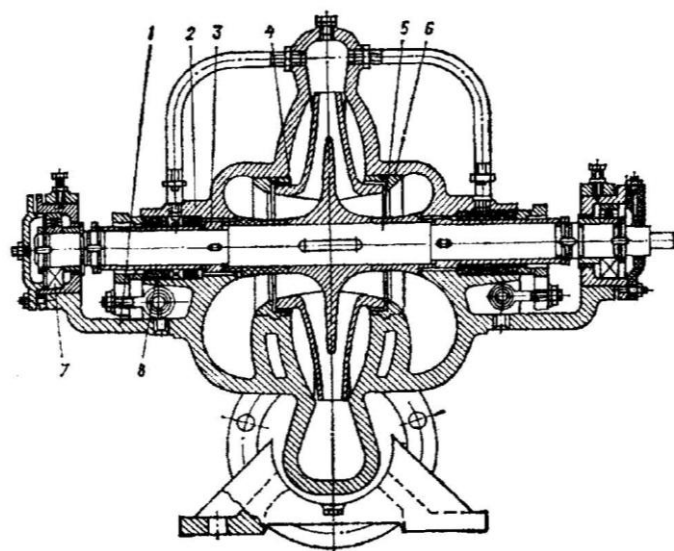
Горизонтальный центробежный насос типа Д: 1 – корпус, 2 – крышка, 3 – защитная втулка, 4 – рабочее колесо, 5 – вал, 6 – уплотнительное колесо, 7 – подшипник, 8 – набивка сальника
